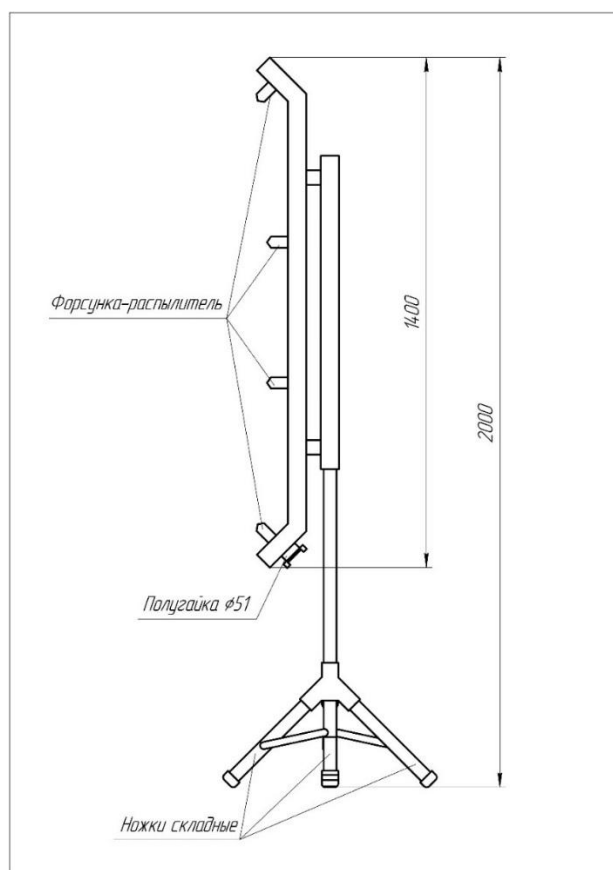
Сборочный чертеж устройства для чистки боевой одежды пожарного
